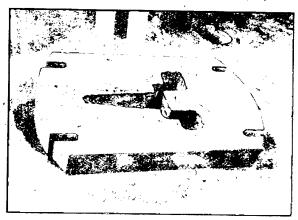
Panzern der Schnittkanten eines Abgratwerkzeuges
